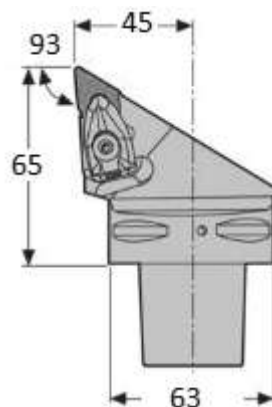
Резец C6-DDJNR-45065-15-M
